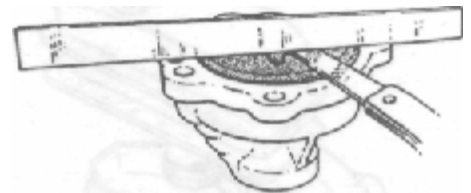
Проверка осевого зазора роторов Двигатель В234F
